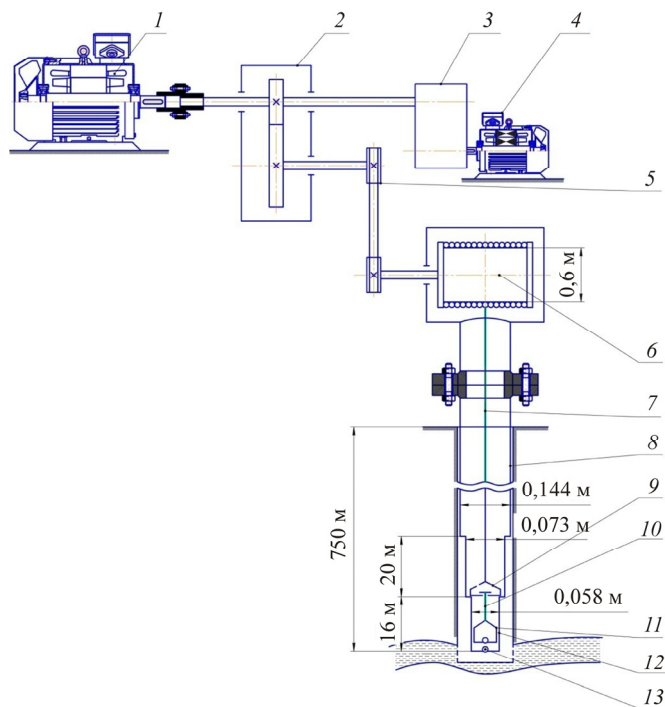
Кинематическая схема электропривода: 1 – асинхронный электродвигатель основного привода; 2 – редуктор; 3 – цепная передача; 4 – барабан; 5 – трос; 6 – труба НКТ; 7 – направляющий центратор; 8 – колонна штанг; 9 – плунжер; 10 – цилиндры насоса; 11 – клапан всасывающий; 12 – гидравлическая тормозная система; 13 – асинхронный электродвигатель гидравлического редуктора
